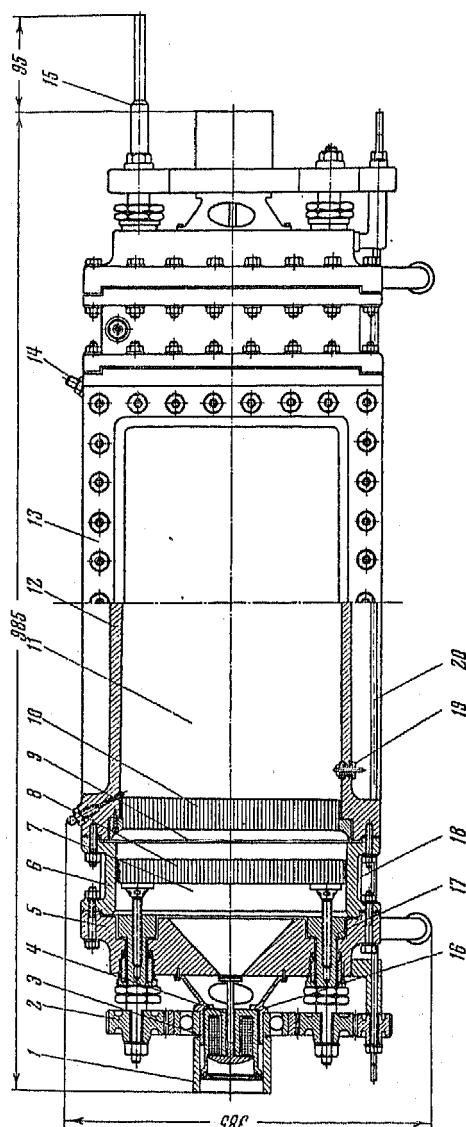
Схема камеры. 1 — магнитный экран, 2 — шестерни, 3 — латунный цилиндр, 4 — клапан, 5 — крышка расширительной головки, 6 — корпус расширительной головки, 7 — расширительное устройство, 8 — подвижная решетка, 9 — резиновая диафрагма, 10 — неподвижная решетка, 11 — стекло, 12 — корпус камеры, 13 — фланец, 14 — шпунер для наполнения рабочего объема, 15 — нониус, 16 — втулка крепления клапана, 17 — механизм для перемещения подвижной решетки, 18 — вводяная рубашка, 19 — ввод «очищающего» поля, 20 — тяга, соединяющая системы шестерен
